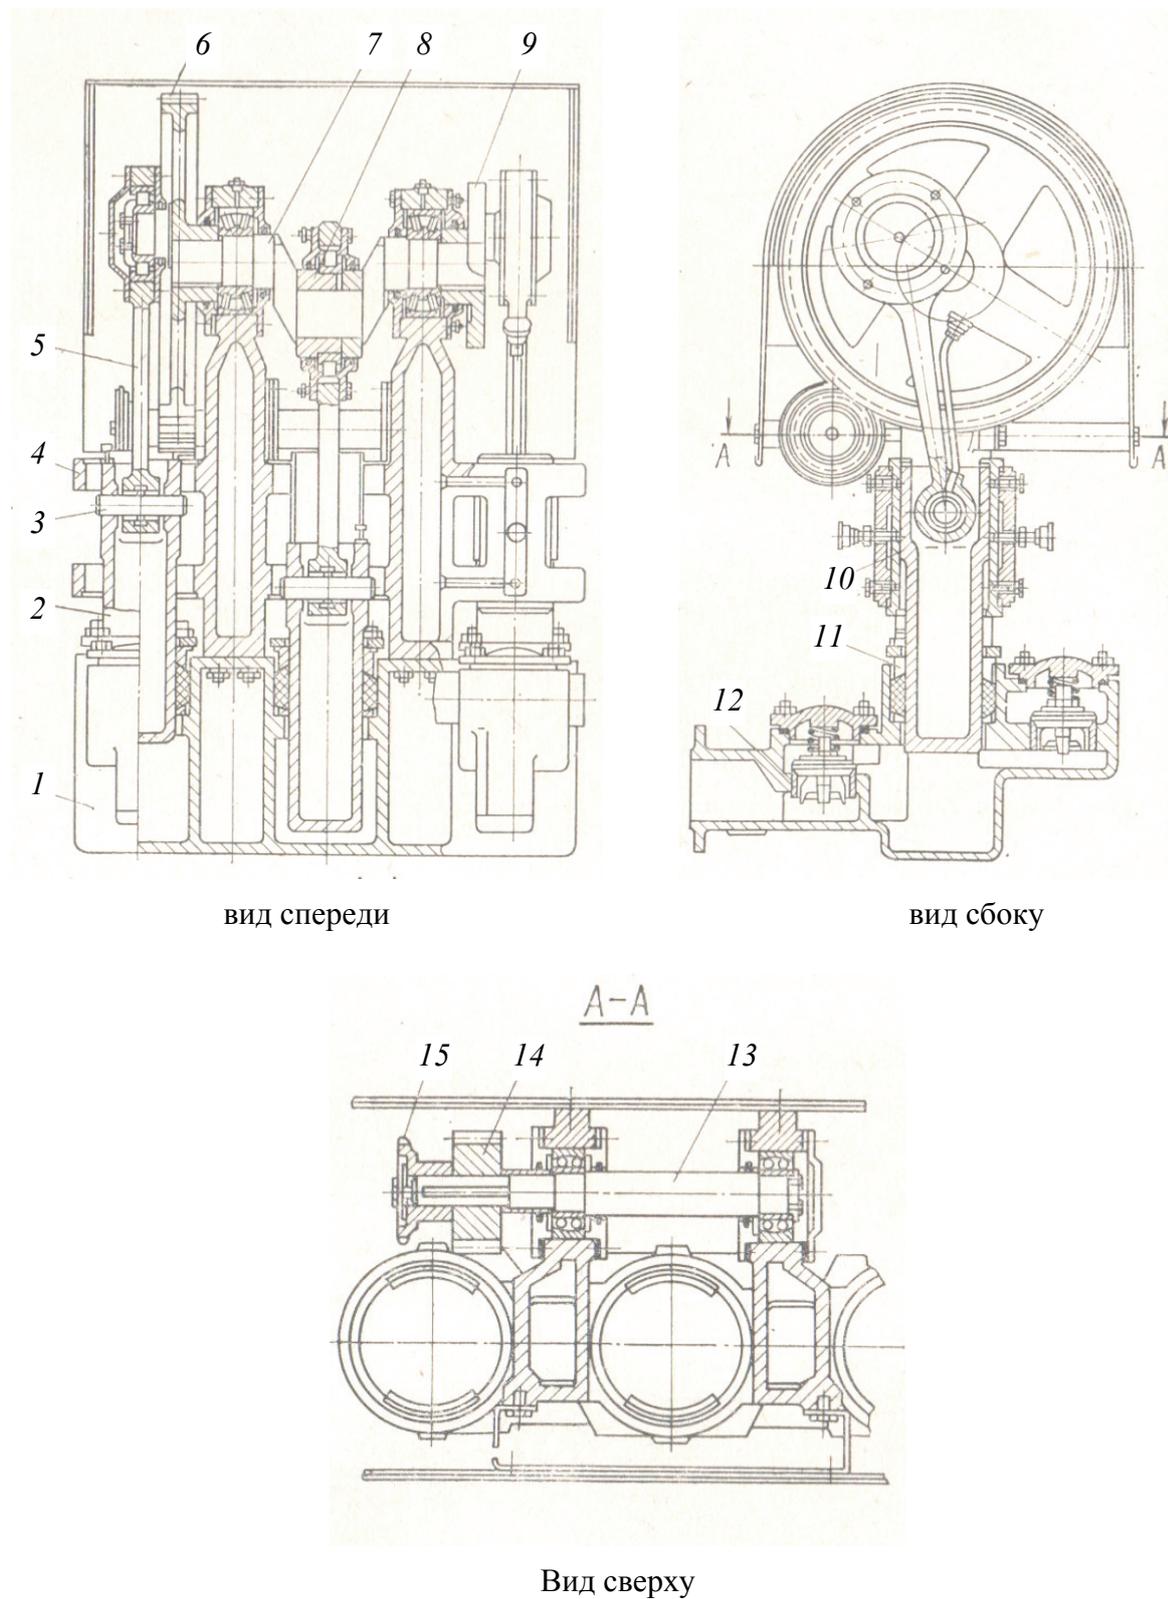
Водоподающий насос 1В: 1 – клапанная коробка; 2 – плунжер; 3 – палец крейцкопфа; 4 – станина; 5 – шатун; 6 – зубчатое колесо; 7 – коленчатый вал; 8 – разрезной вкладыш; 9 – кривошип; 10 – накладка; 11 – сальник; 12 – клапан; 13 – трансмиссионный вал; 14 – шестерня; 15 – полумуфта цепная
